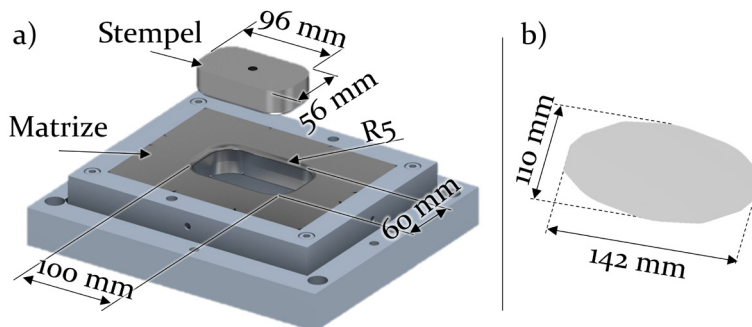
a) Geometrie des unbeheizten Rechtecknapfwerkzeugs und der b) Aluminiumplatte
